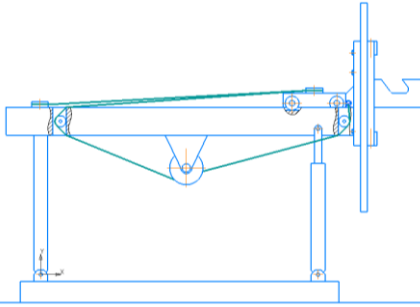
Общий вид установки для извлечения бортовых колец с тросовой системой
